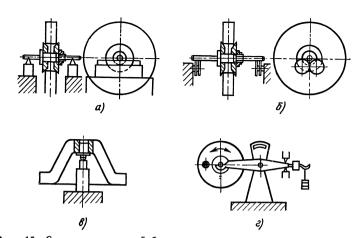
Схемы статической балансировки: a — на призмах; δ — на дисковых роликах; δ — на сферической пяте; ϵ — на весах
